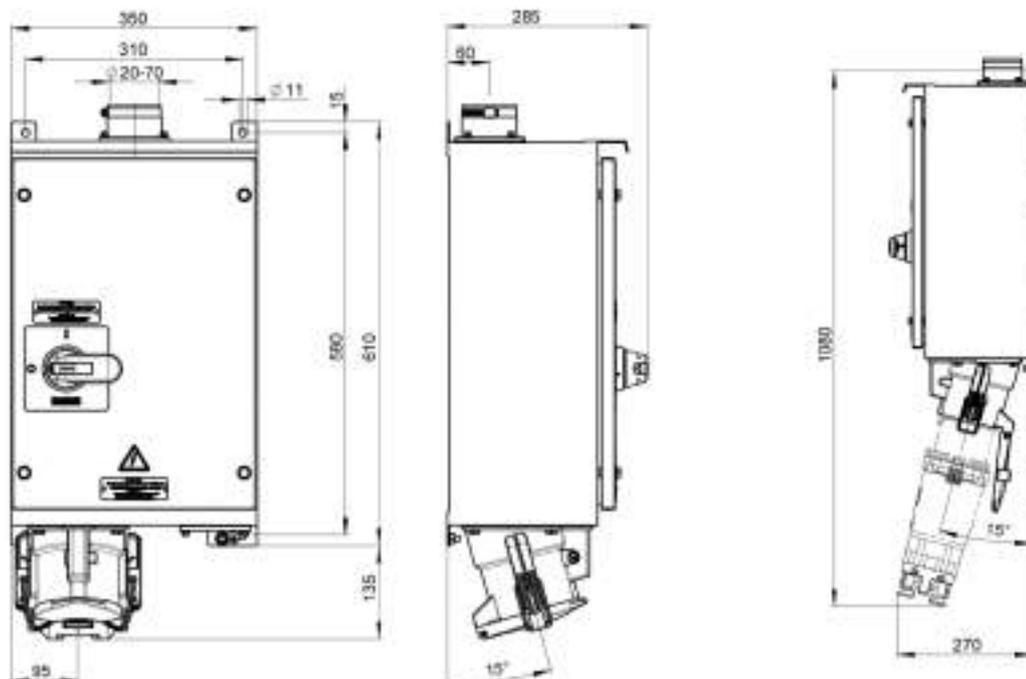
Abmessungen Anschlusskasten mechanisch verriegelt CUMI D-Line, C-Line (160A – 250 A) in mm
